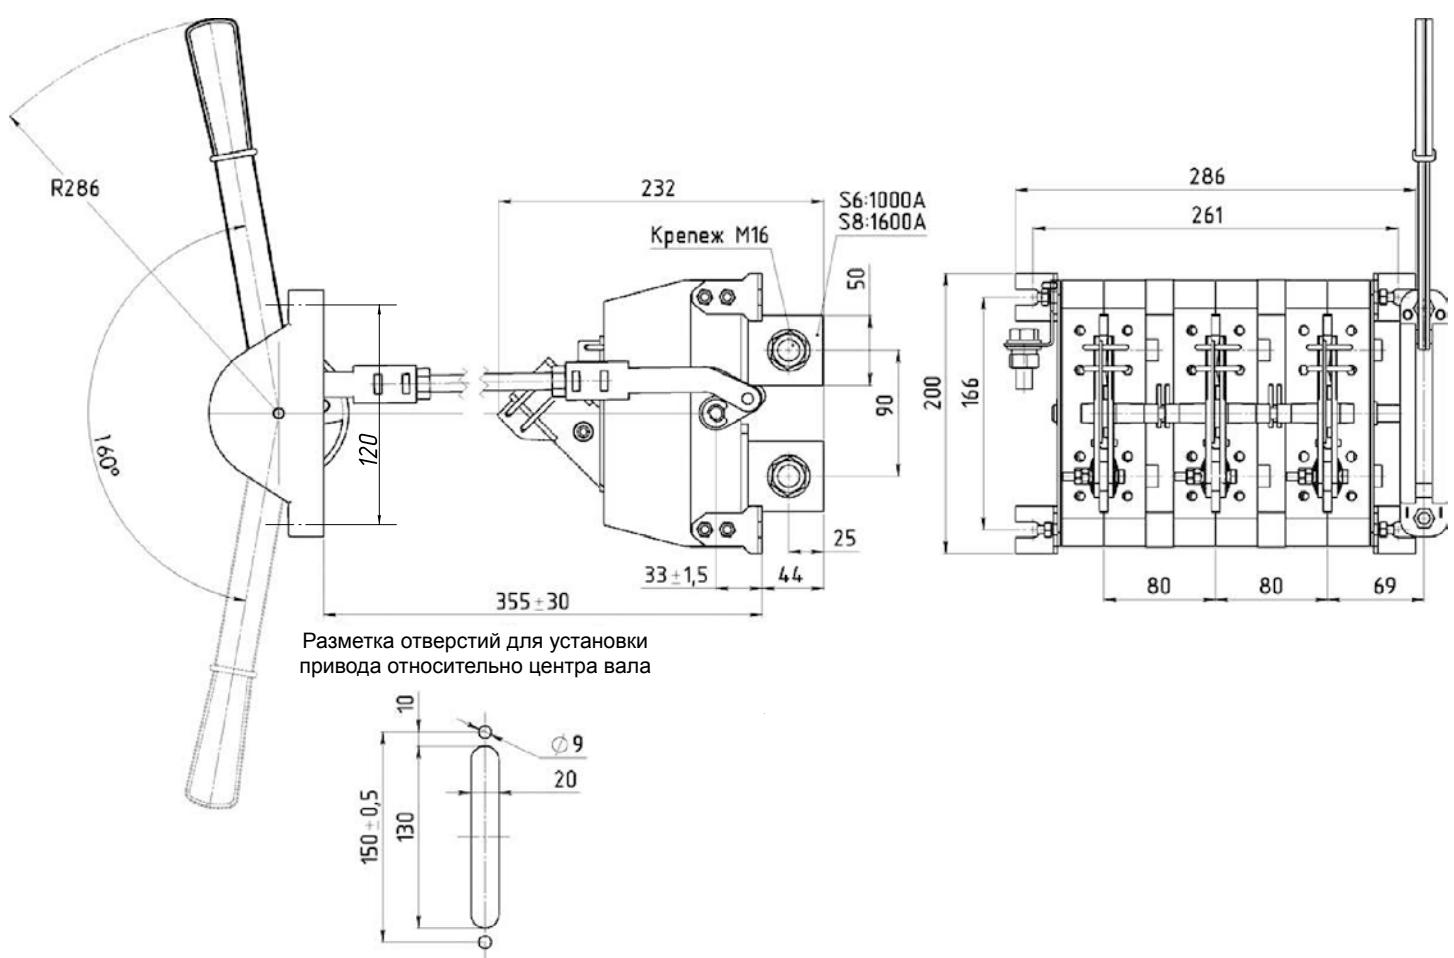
Разъединитель РЕ19-41(43)-32240-00 УХЛЗ с передней смещенной рукояткой, заднего присоединения шин
